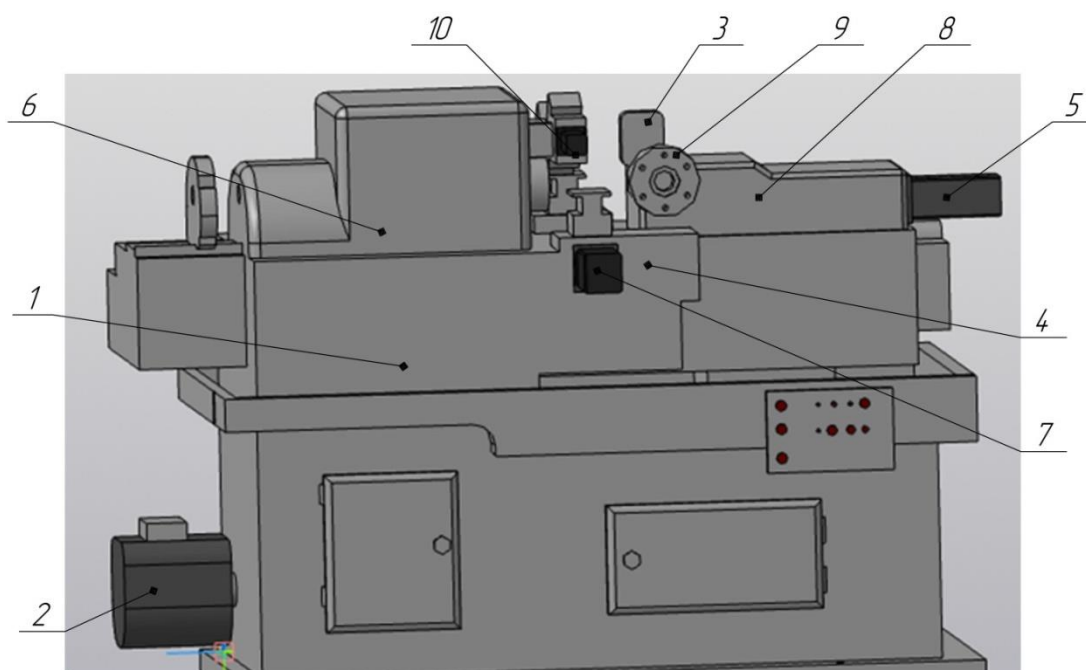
Токарно–револьверний верстат автомат 1Б140 з модернізованими приводами подач: 1–станина; 2–двигун коробки швидкостей; 3–двигун позиціювання револьверної головки; 4–поперечний супорт; 5–серводвигун револьверного супорта; 6–коробка швидкостей; 7–серводвигун поперечного супорта; 8–револьверний супорт; 9–револьверна голівка; 10–серводвигун вертикального супорта.
